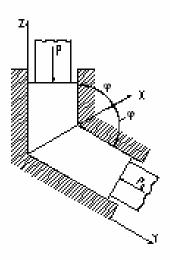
Схема прессования с противодавлением P - давление, созданное пуансоном, P₀ - противодавление, приложенное к выходящему торцу заготовки
